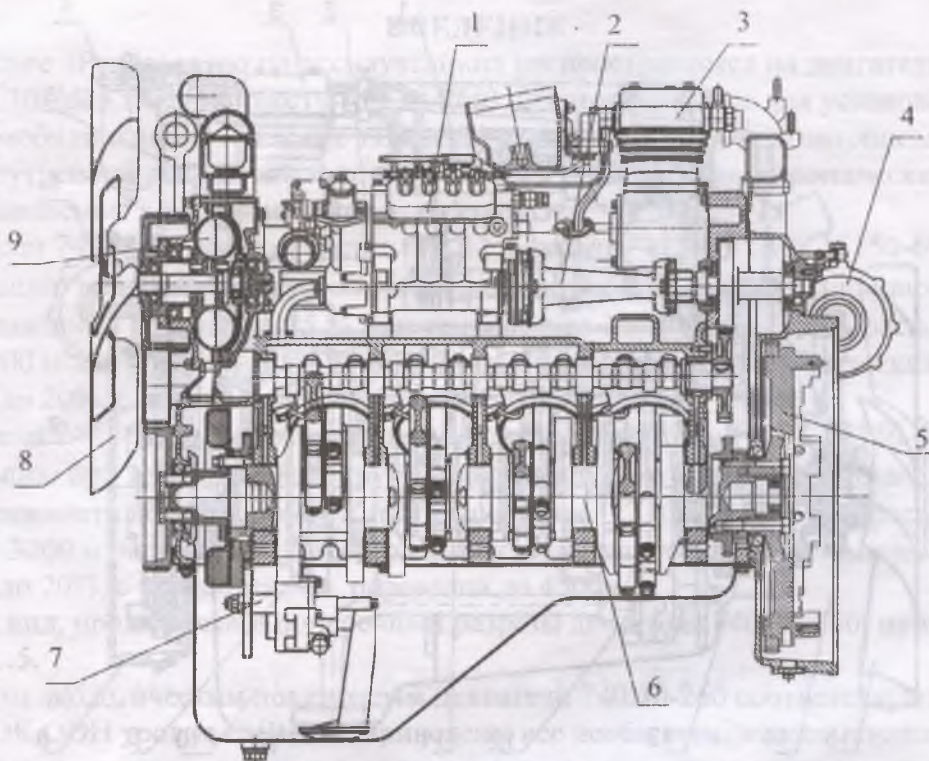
Продольный разрез двигателя 740.30-260 (с верхним расположением вентилятора)
